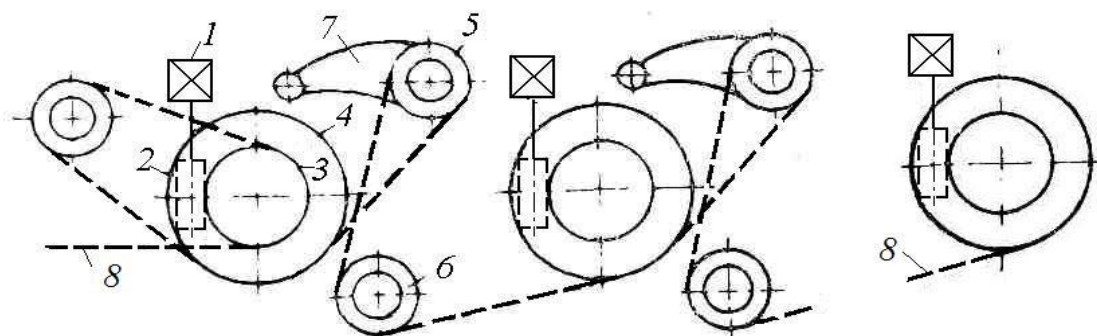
Схема стана петлевого типа: 1 – электродвигатель; 2 – червяк; 3 – червячное колесо; 4 – барабан; 5 – натяжной ролик; 6 – не приводной ролик; 7 – рычаг; 8 – проволока.
